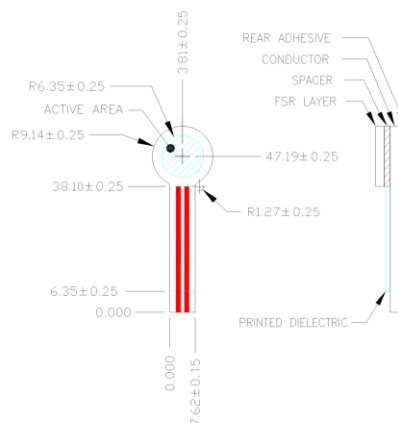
Dimensiones y estructura interna del sensor FSR402 [62].
